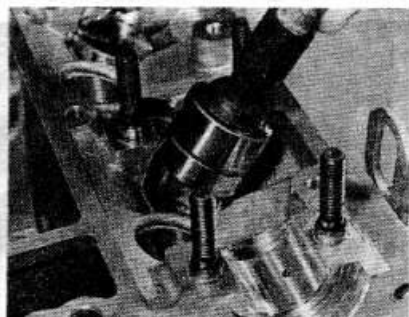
Применение присасывающегося инструмента типа резинового плунжера для снятия толкателей клапанов — двигатель с двумя распредвалами
